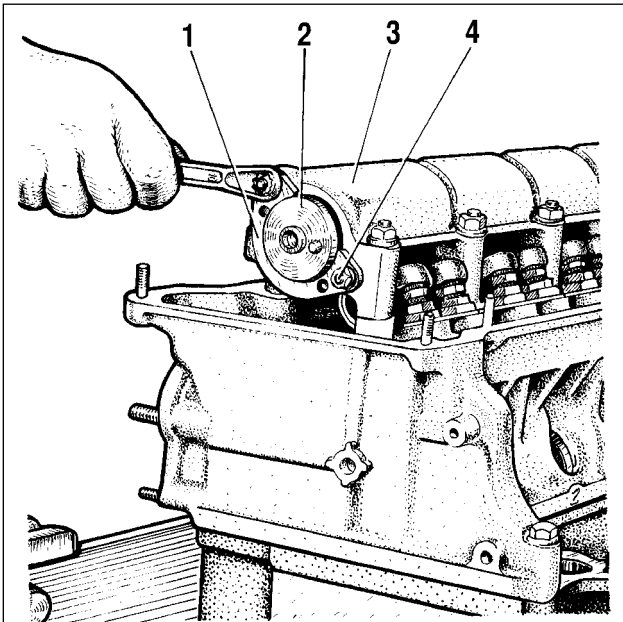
Ausbau des Anschlagflansches der Nockenwelle:
